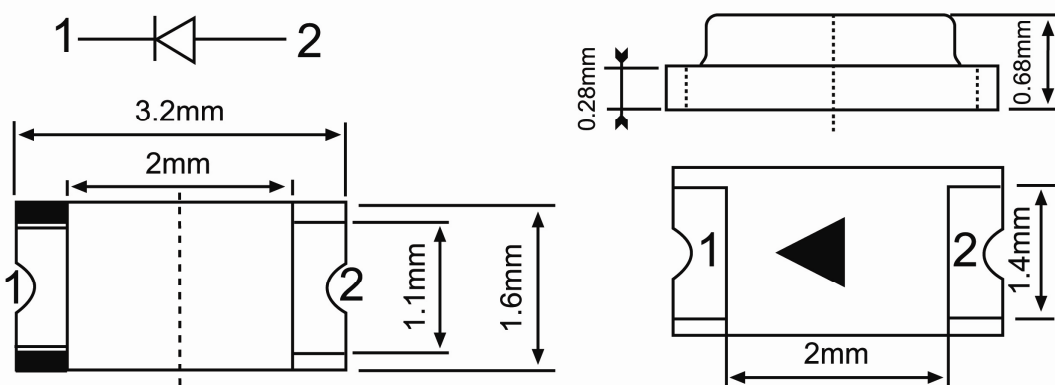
Esquema dimensionado de um LED SMD 1206.
